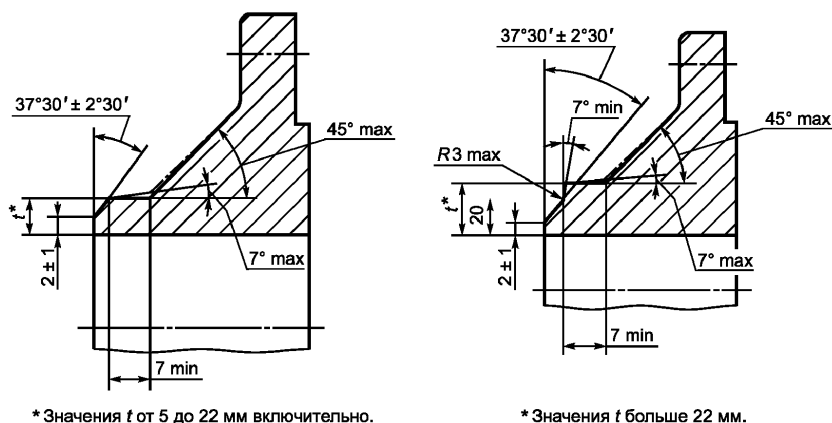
Разделка кромки под сварку для фланцев типа 11, ряд 2
